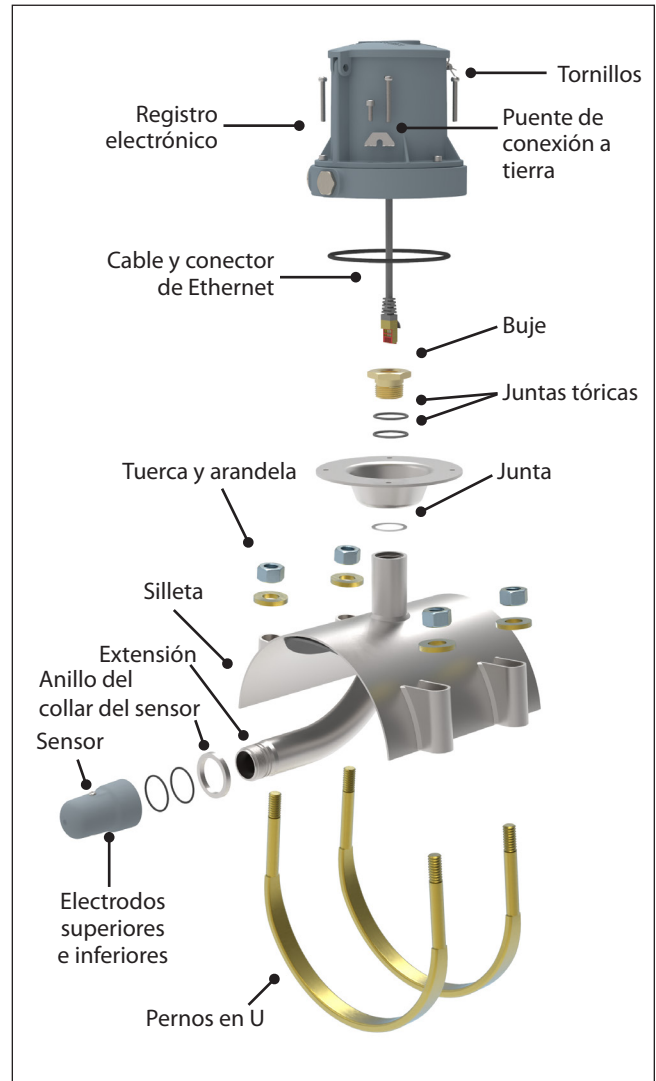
Ensamblaje de McMag²⁰⁰⁰
